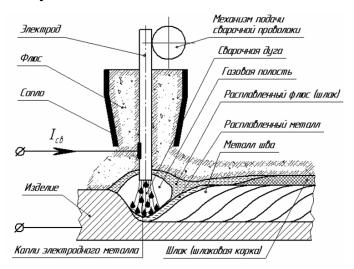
Схема дуговой сварки под слоем флюса
